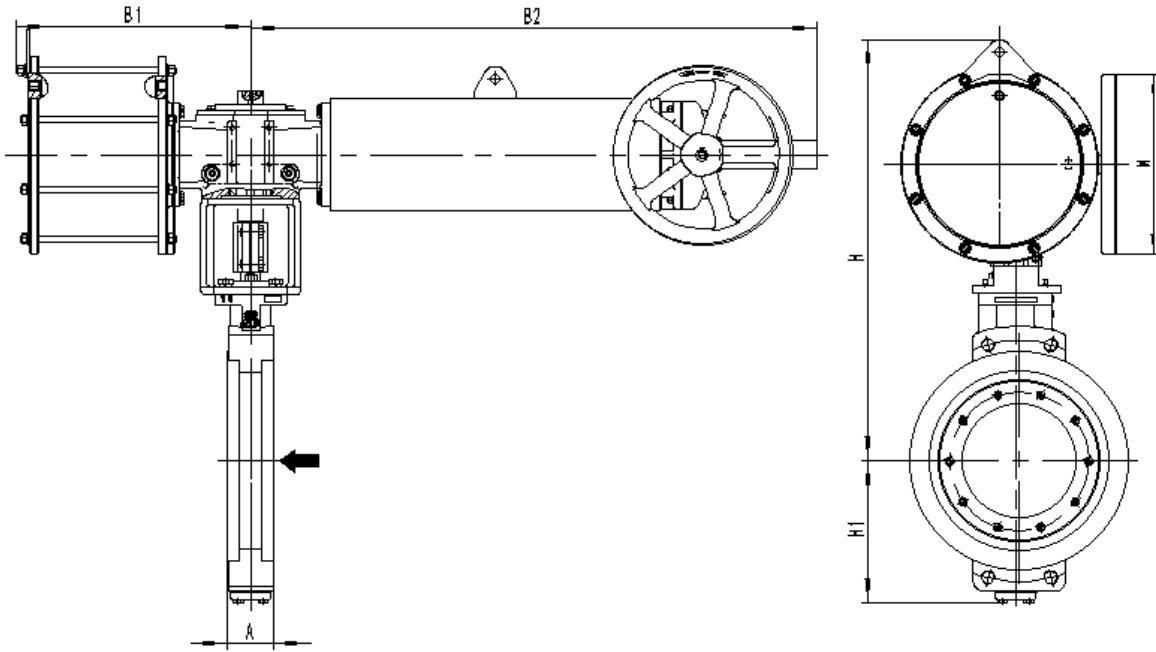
配 AW30SR42~AW40SR53 带伞齿手轮外形尺寸图 (FC)
